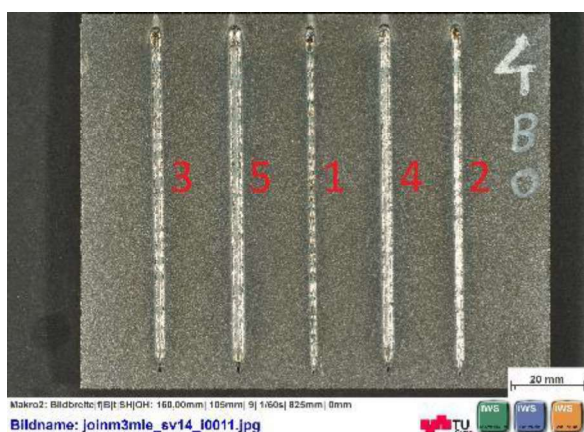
Platte 04 Blind Oberseite mit Schweißnahtkennzeichnung
